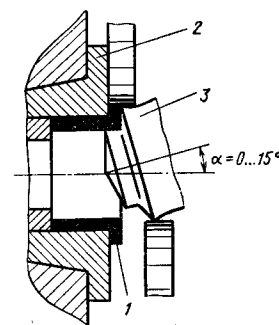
Схема торцовой раскатки: 1 — заготовка; 2 — матрица; 3 — раскатной валок
